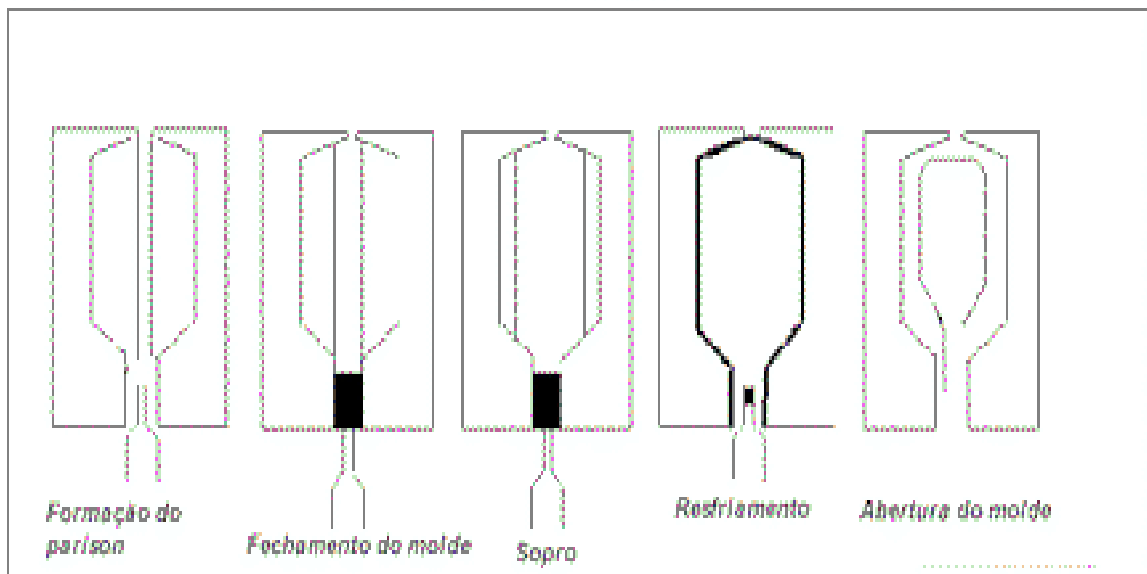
Ilustração do processo de moldagem por sopro via extrusão
